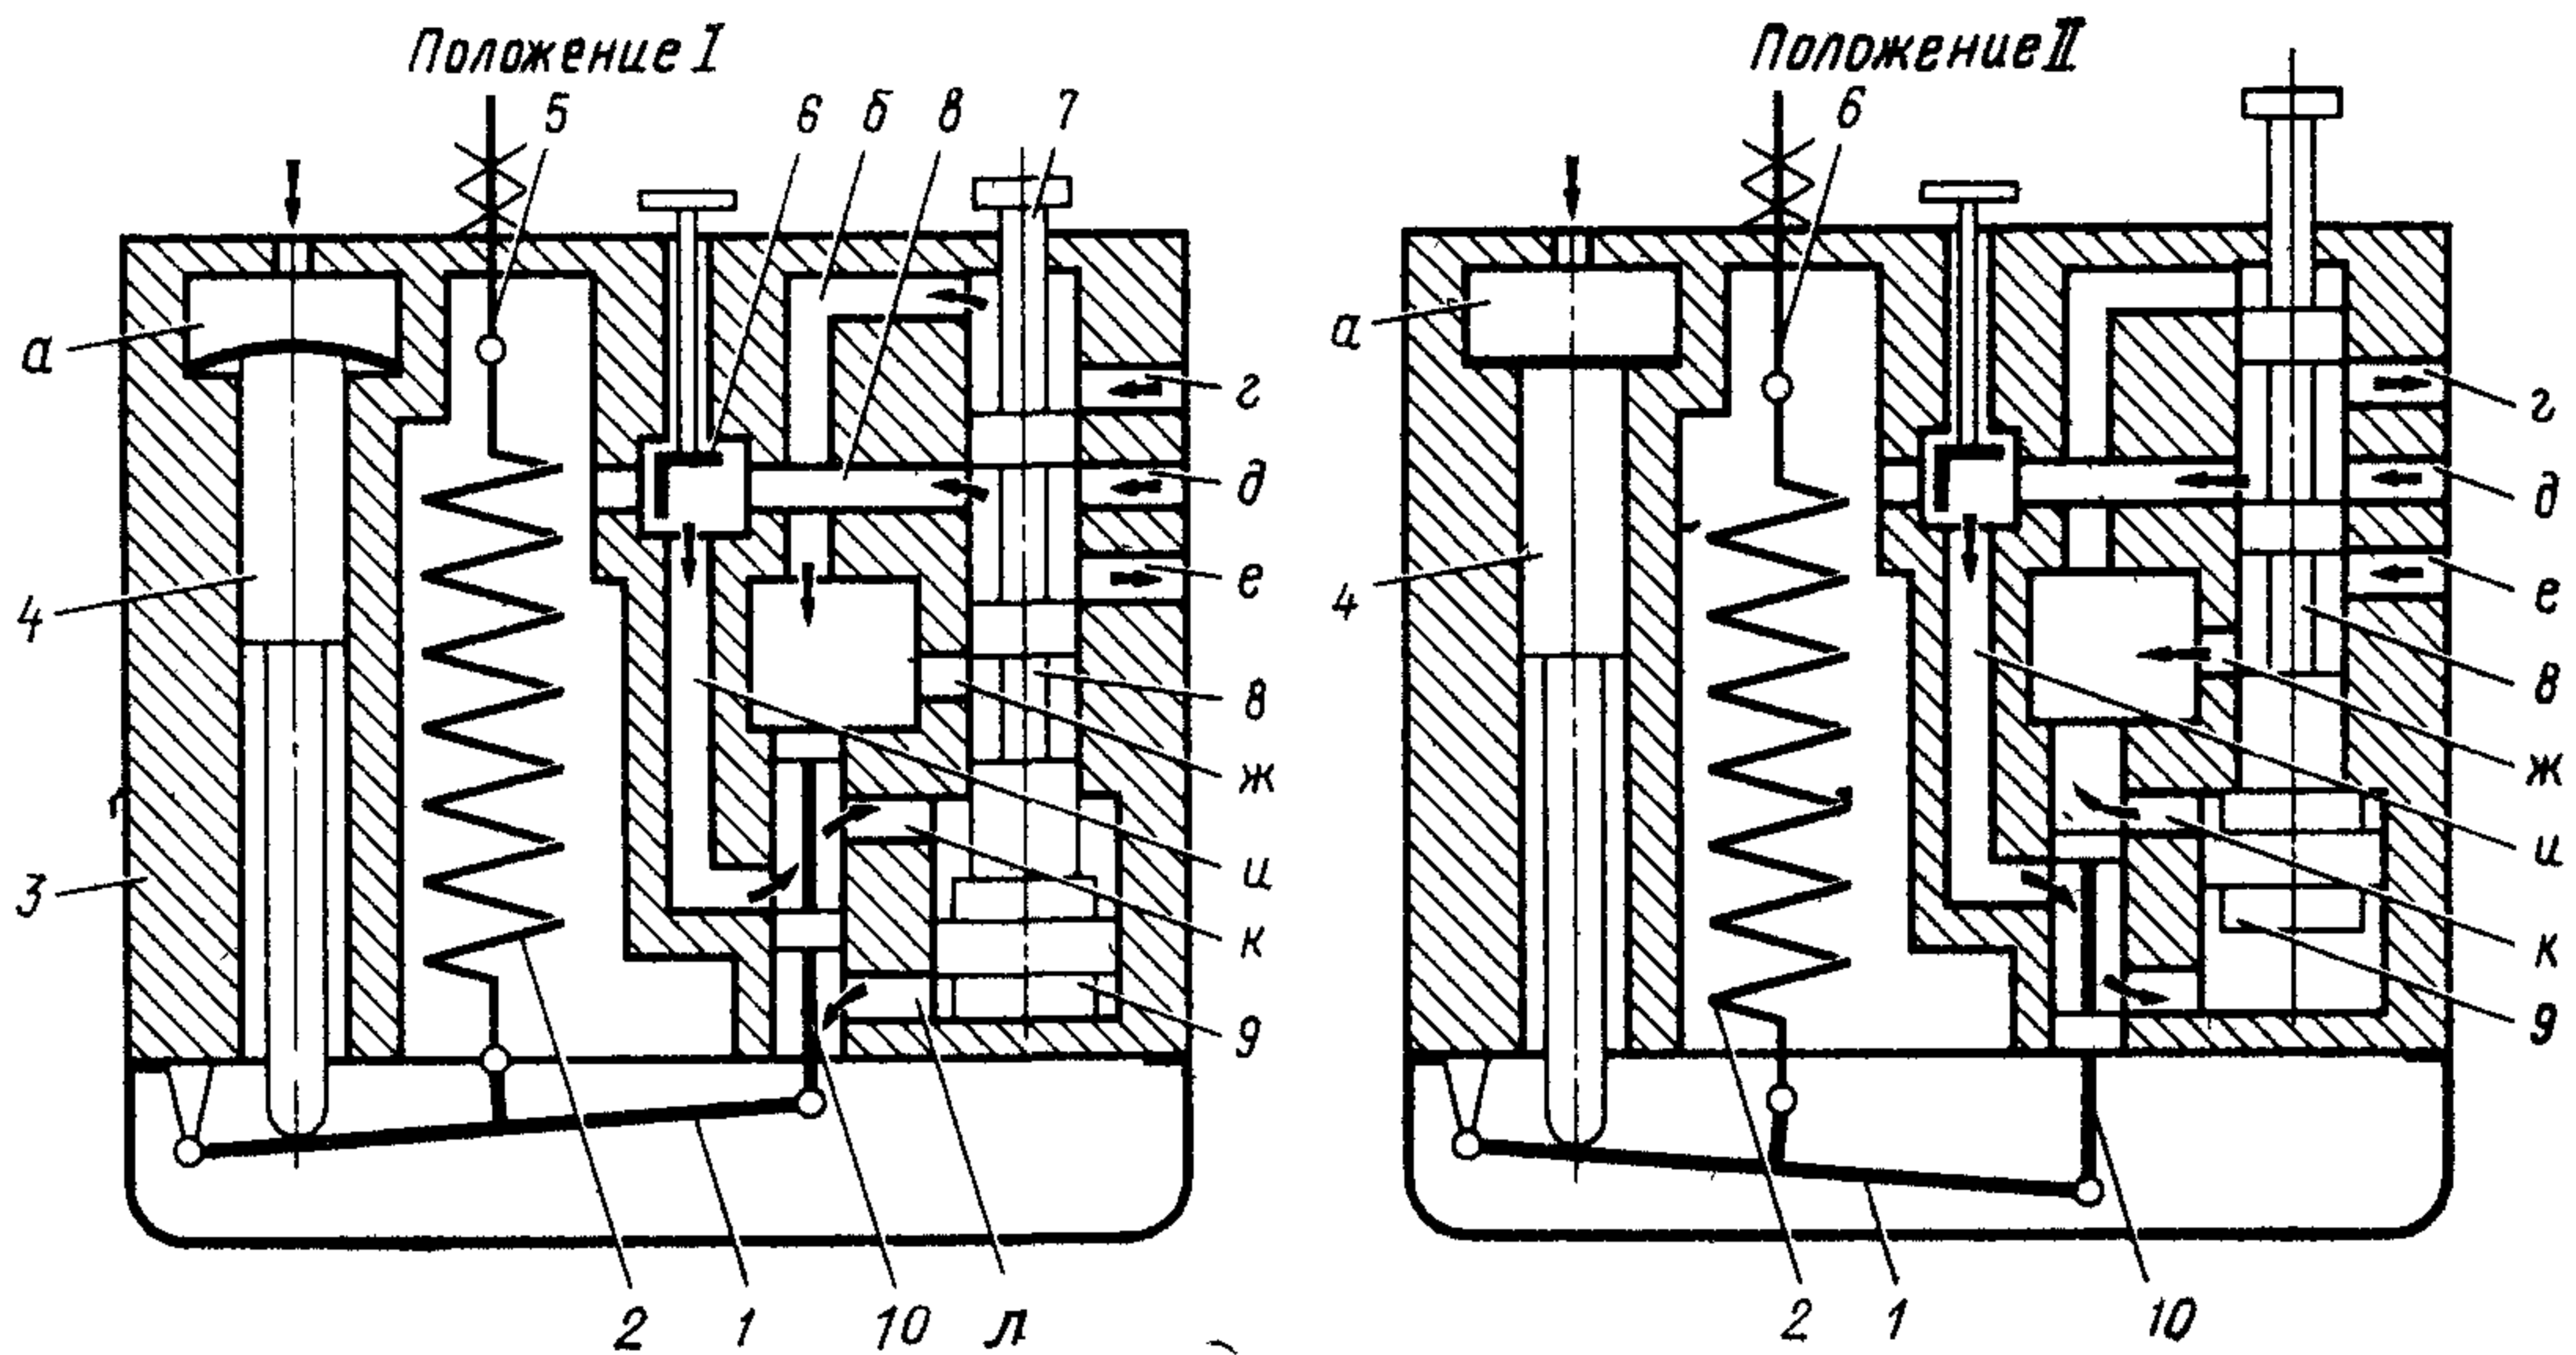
Схема автоматического устройства выключения компрессора двигателя 6Л275ПН
